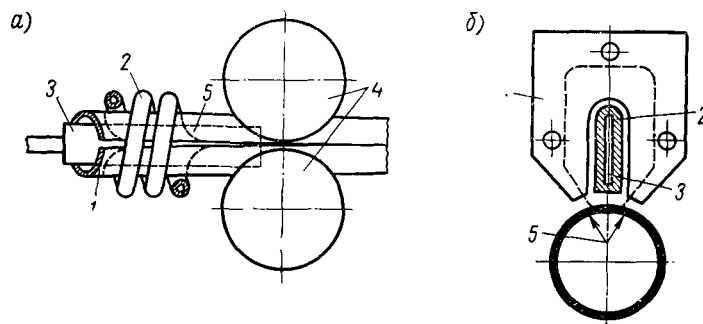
Схемы индукционной сварки труб:
